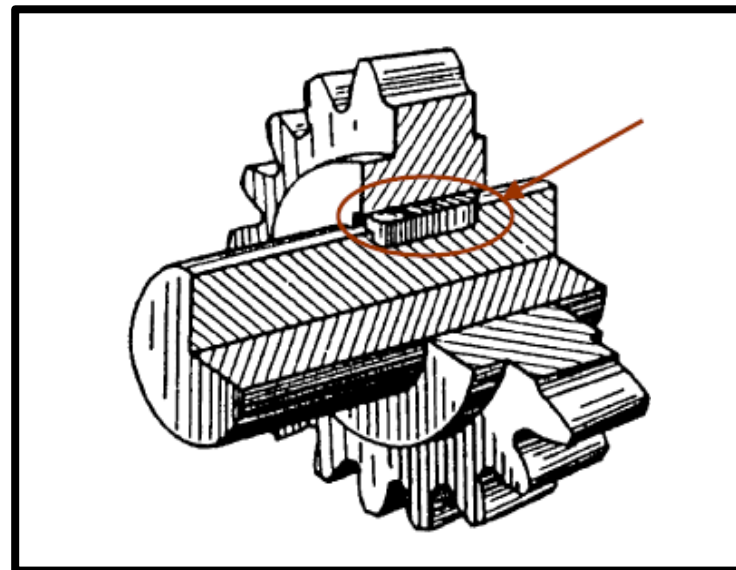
fissaggio albero-mozzo mediante chiavetta.
